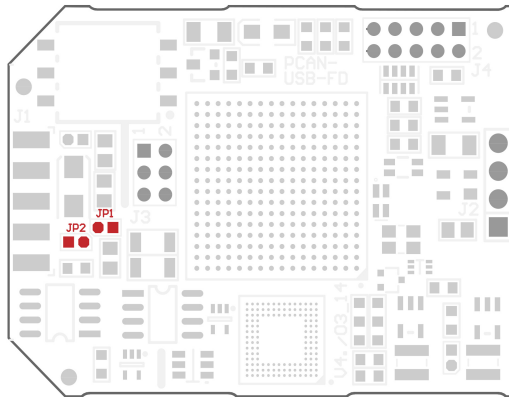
Draufsicht Platine PCAN-USB FD Lötpfelder JP1 und JP2
